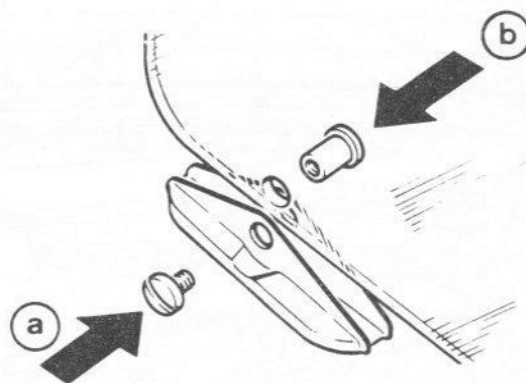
Vis (a) et manchon (b) de pose des tampons de guidage sur la glace de custode – modèles Cabriolet (Sec 21)
